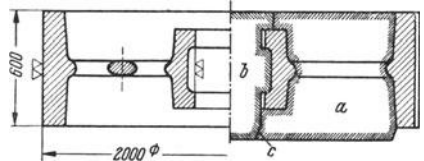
Schwungrad mit 6 Armen (Werkzeichnung und Werkaufriß). *a* = Armkern; *b* = Bohrkern; *c* = Kegel.
